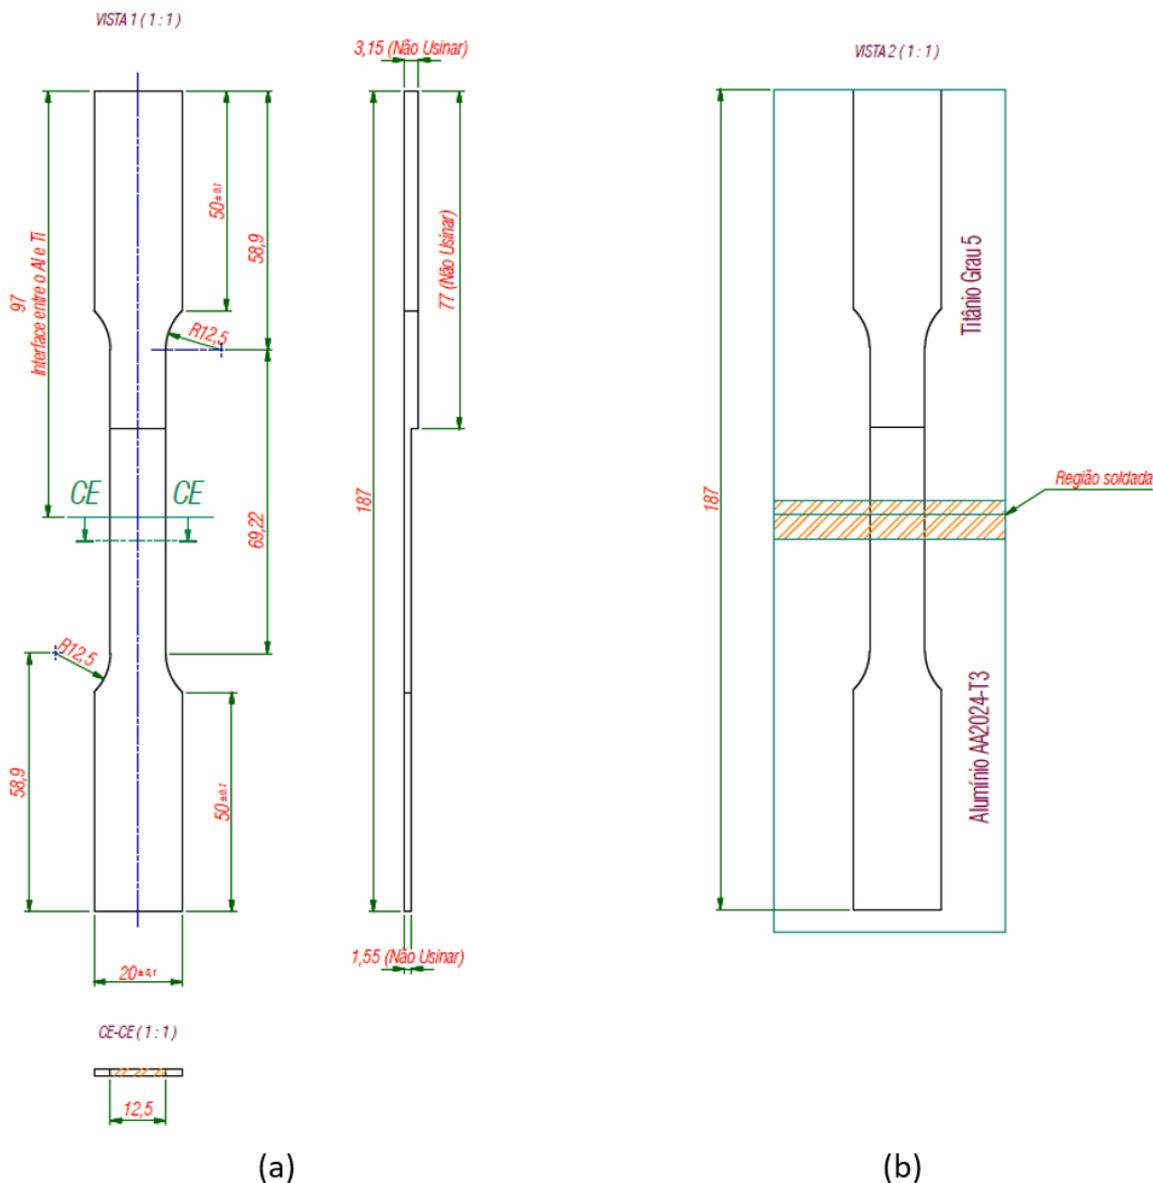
Desenho do corpo de prova adaptado o esquema da norma ASTM E8 “Standard Sheet Type, 12.5 mm” para ensaios de tração da junta soldada na condição de chapas finas. (a) Corpo de prova. (b) Região de retirada do corpo de prova em relação às chapas soldadas.
